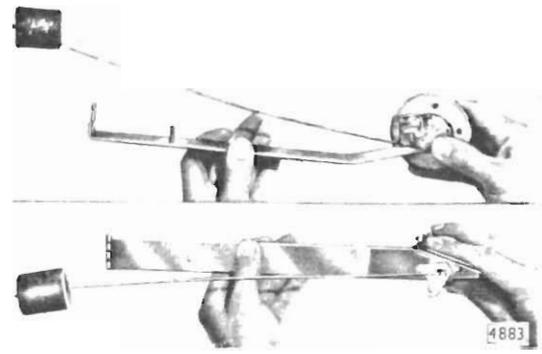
Verbogener Schwimmhebel mit Prüfllehre
